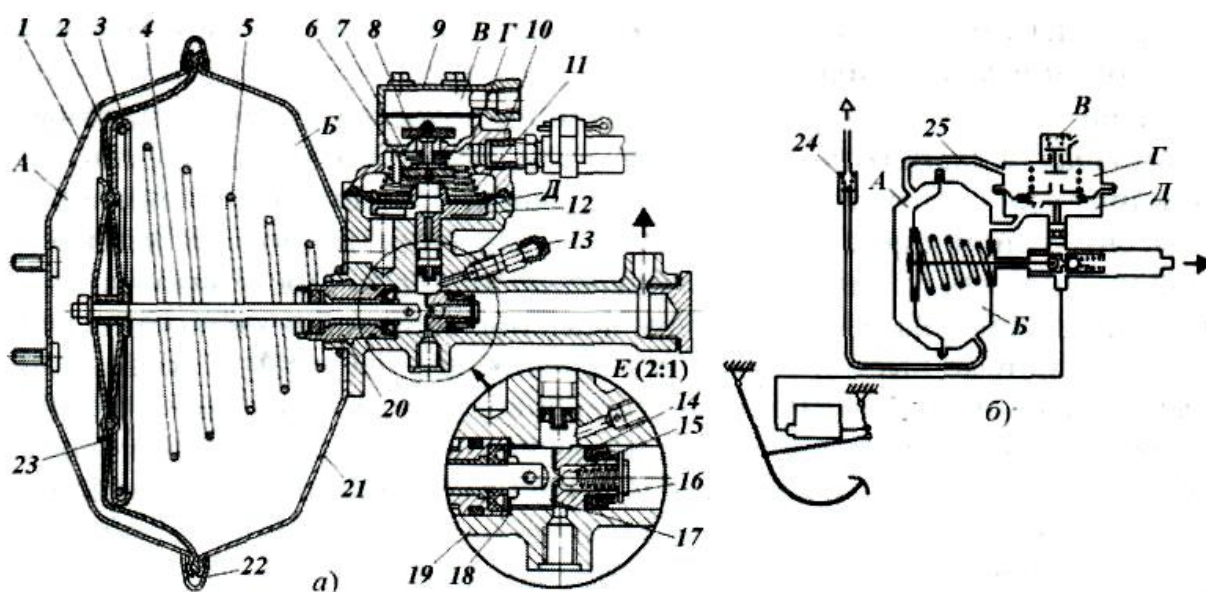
Гидровакуумный усилитель: а — чертёж; б — принципиальная схема
